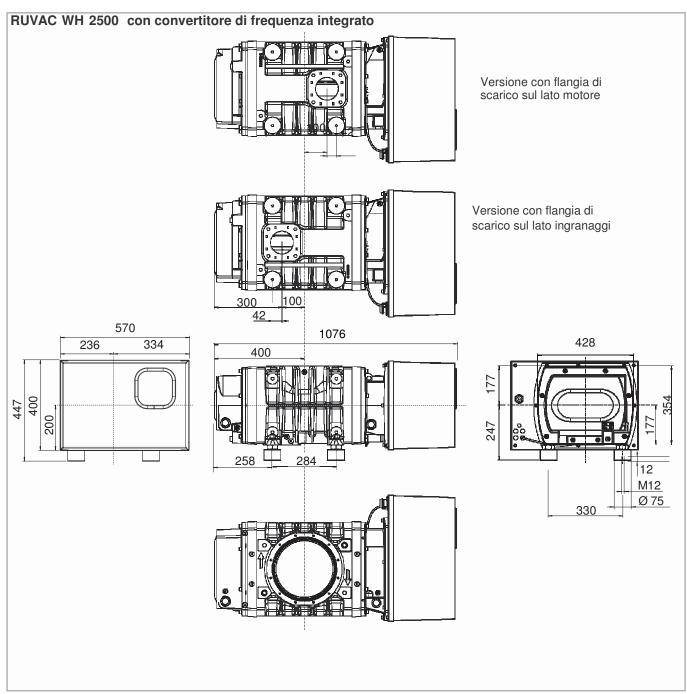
Disegno dimensionale per la RUVAC WH/WHU 2500 con convertitore di frequenza integrato
